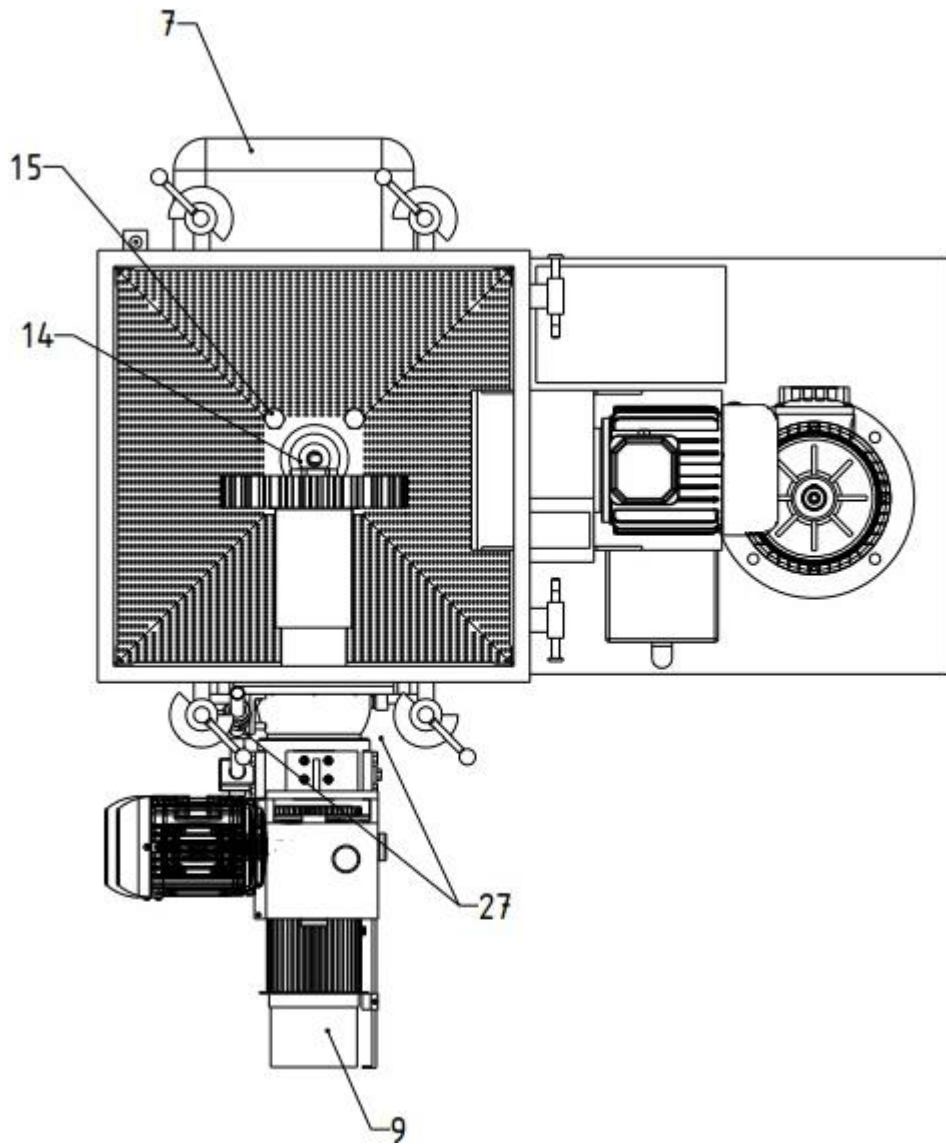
Установка для ГДУ (вид сверху)
